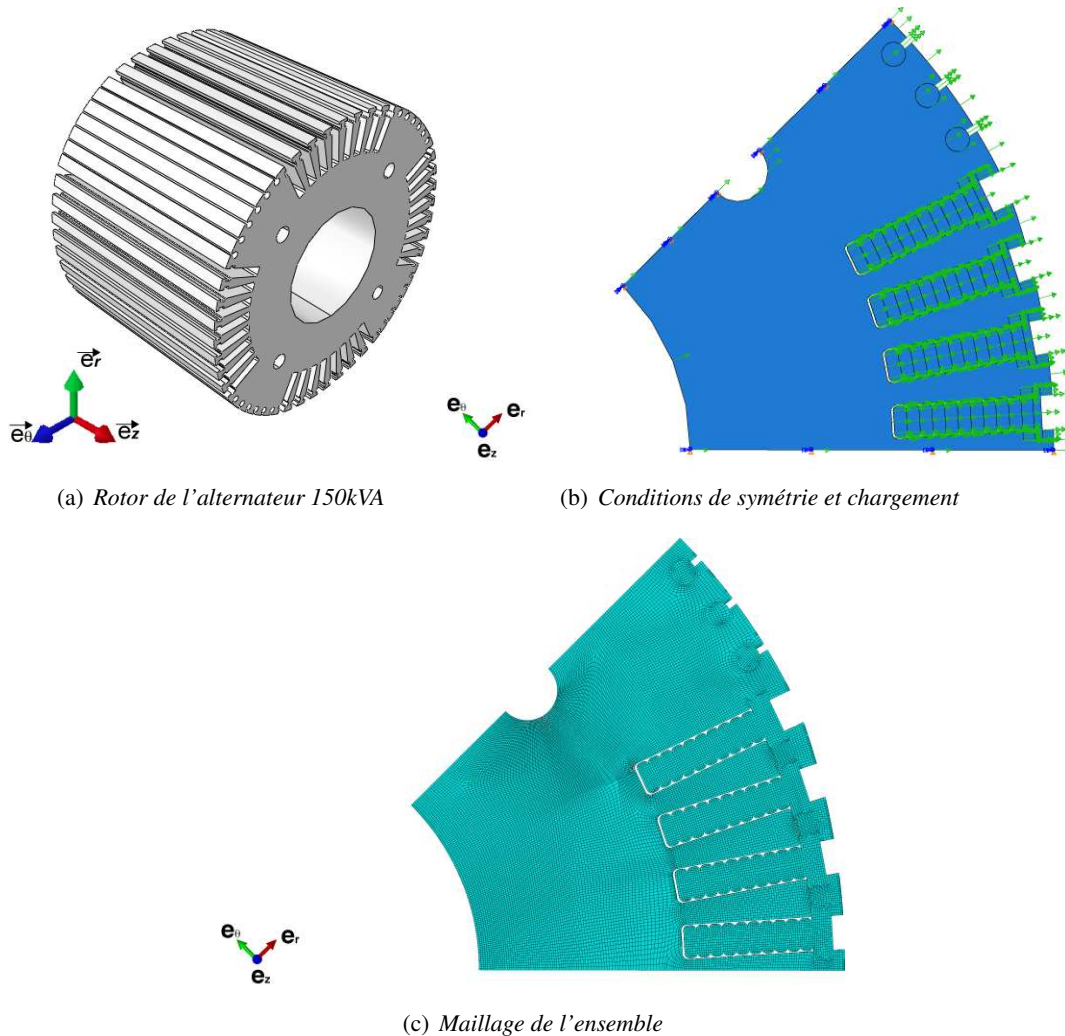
Exemple d'un rotor de machine à grande vitesse.
